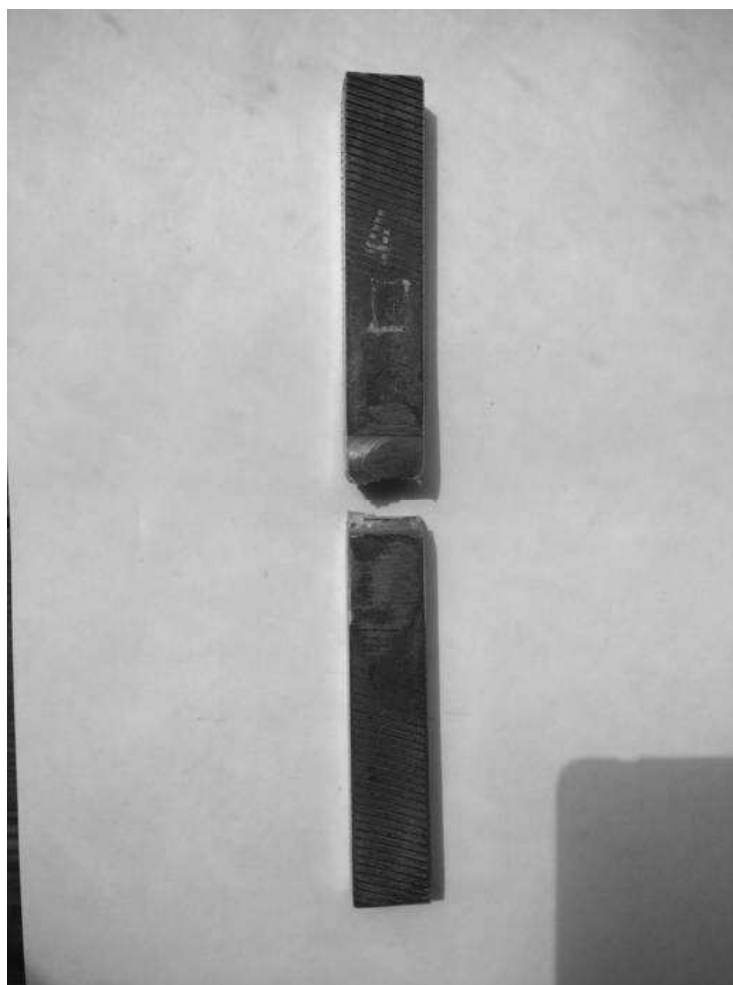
Разрыв по сварному шву стали WELDOX 700E.
